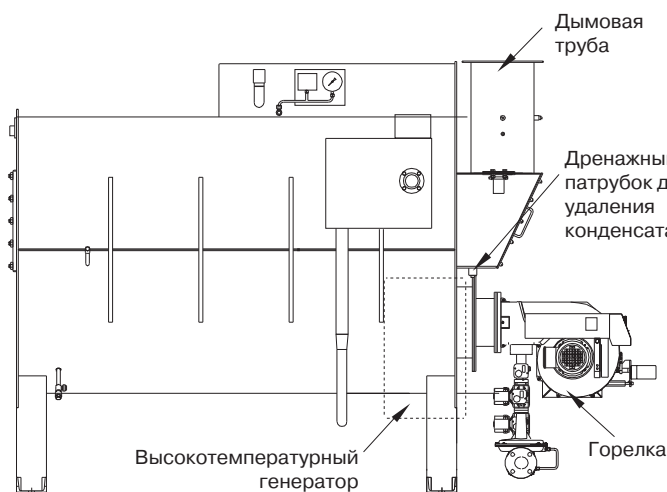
Расположение дренажного патрубка для удаления конденсата
